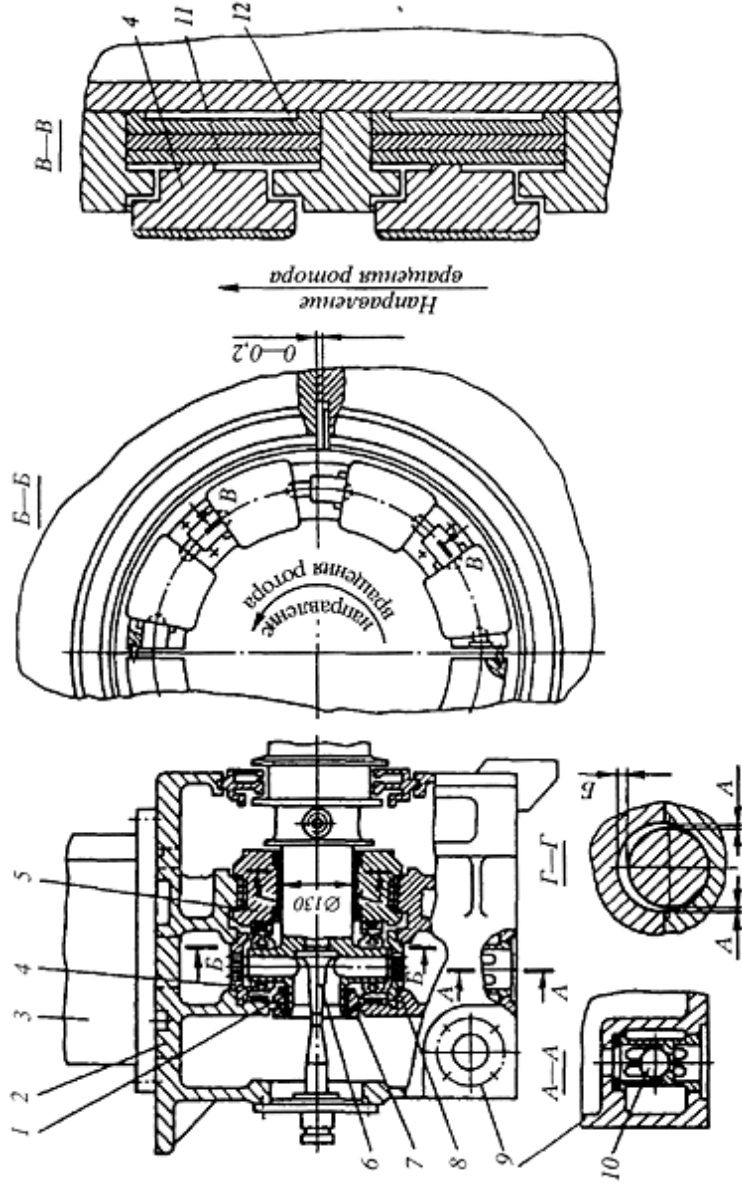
Опорно-упорный подшипник конструкции КТЗ: 1 – рабочее колесо главного масляного насоса; 2 – крышка подшипника; 3 – блок регулирования; 4 – колодки упорного подшипника; 5 – вкладыш опорного подшипника; 6 – обтекатель; 7 – плавающее уплотнительное кольцо; 8 – направляющий аппарат (сетка); 9 – корпус подшипника; 10 – обратный клапан; 11, 12 – опорные пластины
